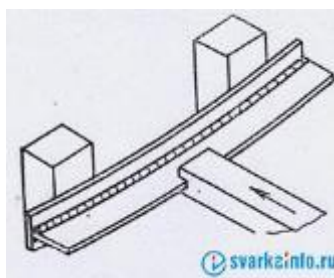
Схема исправления сварной тавровой балки путем приложения статической нагрузки
